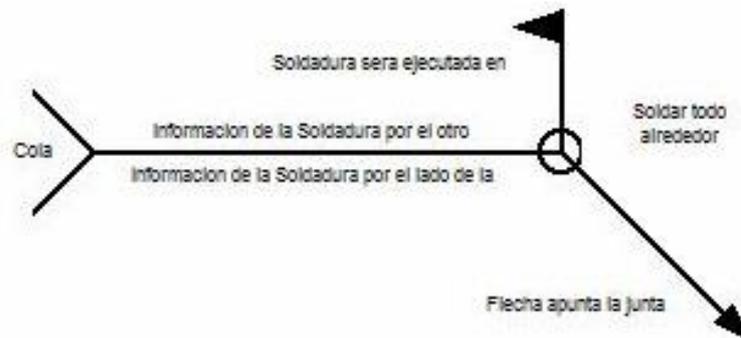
Estructura de la simbología de la soldadura.
